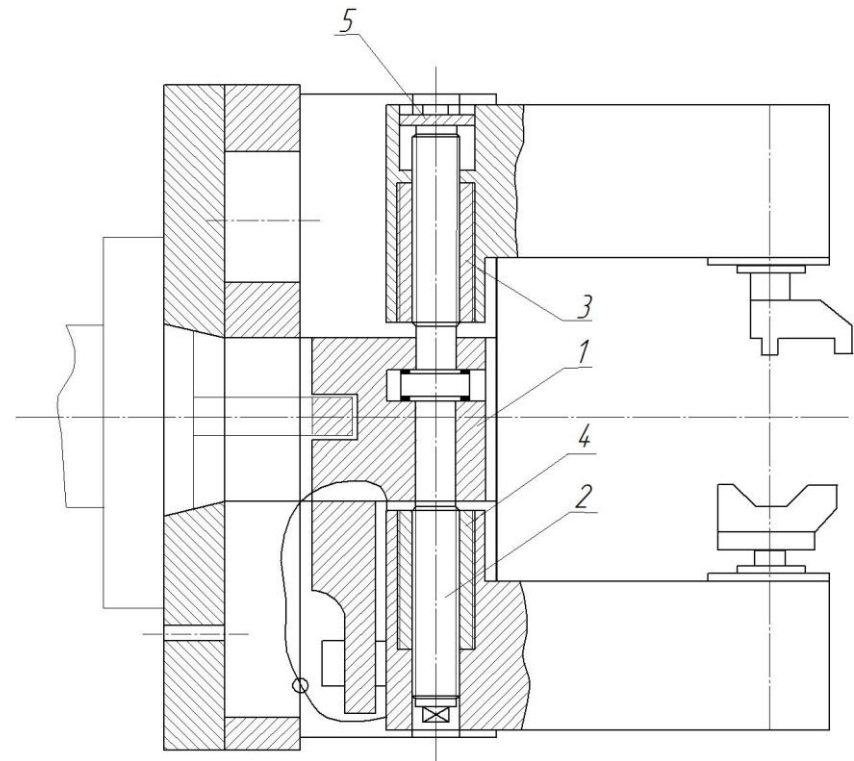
Конструкция поворотного патрона с винтовым устройством зажима
